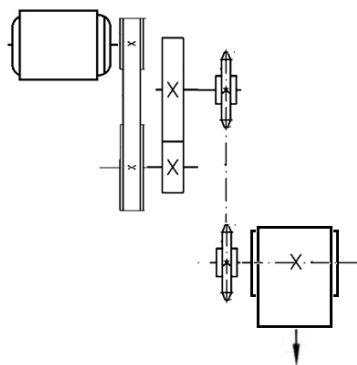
Кінематична схема приводу стрічкового конвеєра
